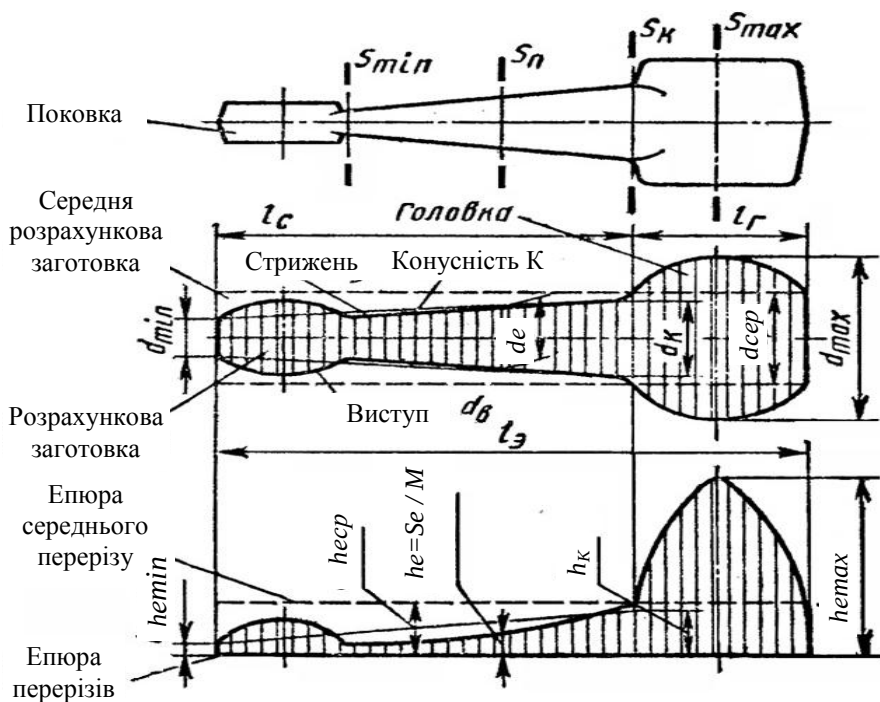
Елементарна розрахункова заготовка та епюра перерізів
